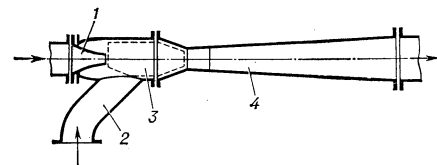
Схема струйного насоса: 1 — конический сходящийся насадок; 2 — всасывающий патрубок; 3 — камера смешения; 4 — диффузор.
